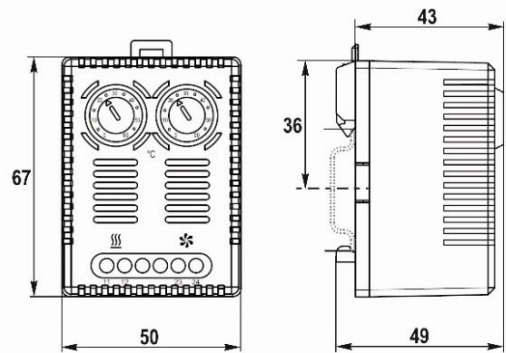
б – Общий вид и габаритные размеры терморегулятора UNISPLIT 71NCNOF01
